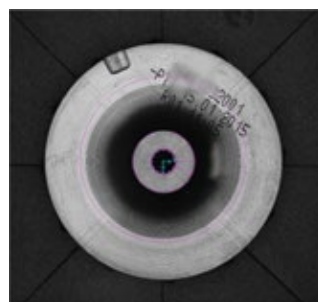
Station 2 – Prüfungen für den Radrücken (Kamera 16 MP, Auflösung 20 µm): Austritts- und Außendurchmesser, Planfläche RR Außen- und Innen-Durchmesser, Phase Planfläche RR, Oberflächenfehler Planfläche RR, Beschädigungen Kanten Planfläche RR und Außenkante (Ausblendung Wuchtentnahmen), Oberflächenfehler RR
